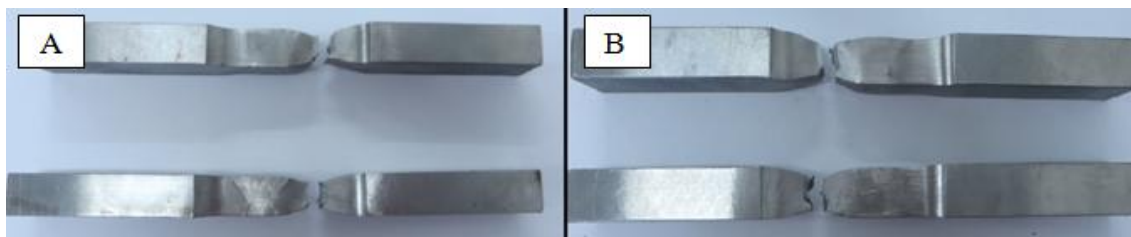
Ensaio de tracção - Local de fractura nos provetes soldados pelo fio
